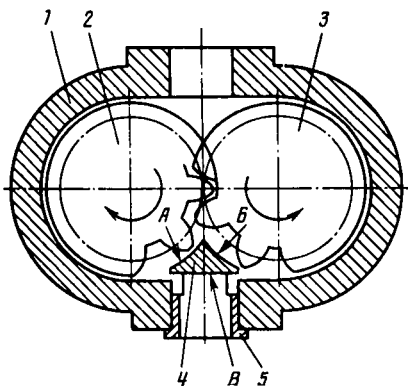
Схема шестеренного гидромотора с устройством для улучшения пуска:
